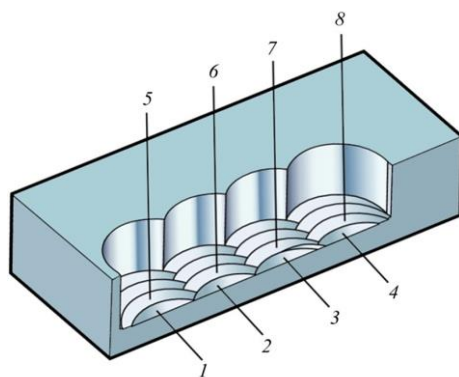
Оброблення вибірки від дна з поступовим підняттям різального інструменту при плунжерному фрезеруванні [5]
